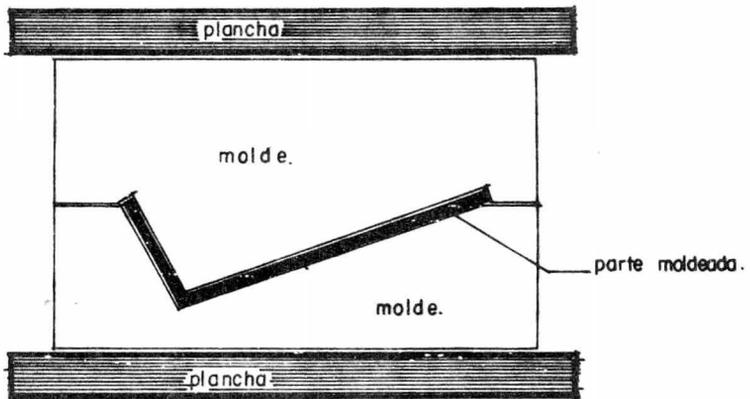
REFORZADO.- MOLDEO DE PREMEZCLAS.
